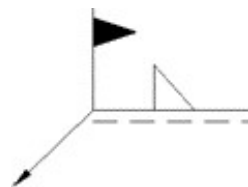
Modo de representación de una soldadura realizada en el lugar de montaje
